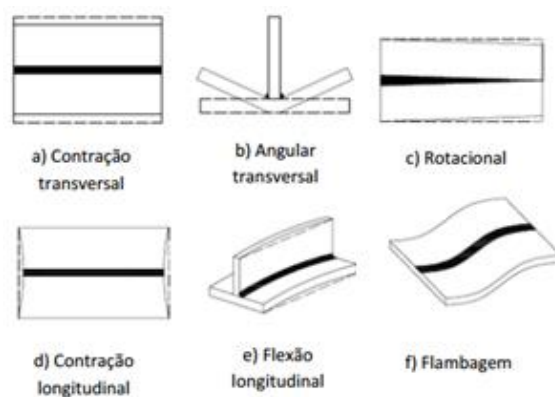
Principais tipos de distorções causadas por processos de soldadura [60].
